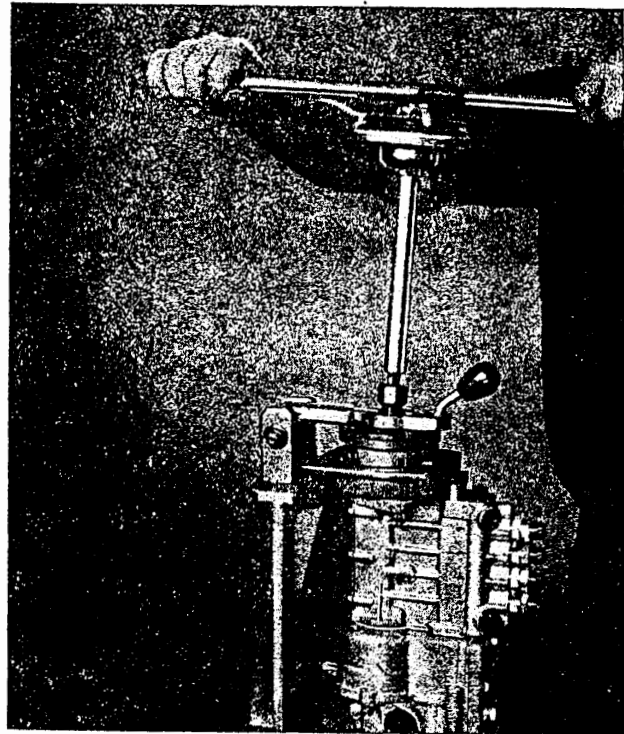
Befestigungsmutter des Spritzverstellers mit Spezialschlüssel (Werkzeug Nr. 324.020-M 117) und dem Drehmomentschlüssel 50 ... 60 Nm (5 ... 6 kpm) anziehen
